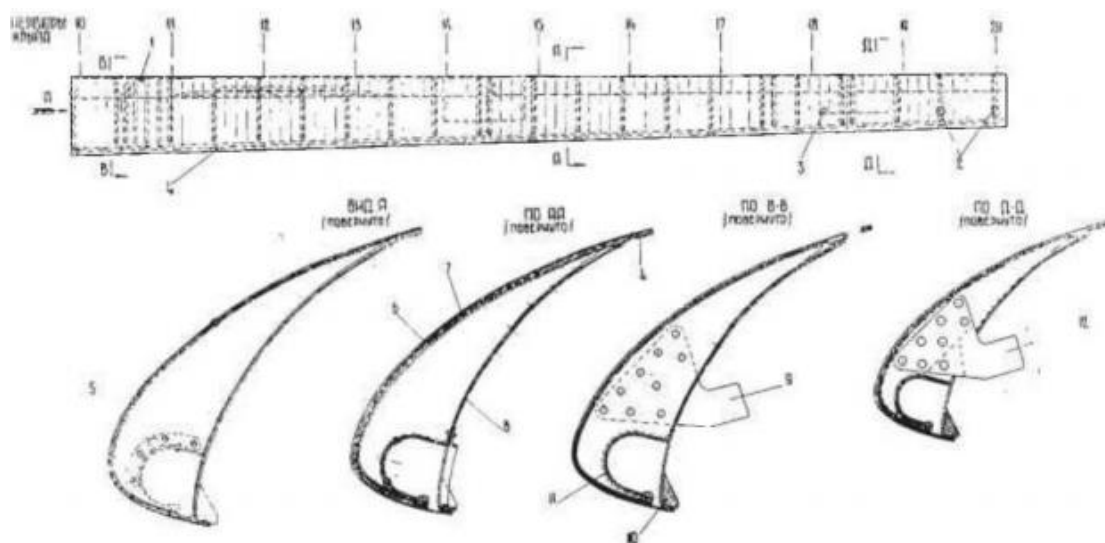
Предкрилок консольної частини крила (1 секція): 1-гофр; 2-нервюри; 3- дуралюмінієві прокладки; 4-прокладки з полімідної смоли; 5- окантовка; 6-верхня обшивка; 7-гофр; 8 нижня обшивка; 9-кронштейн на нервюрі 11; 10- прокладка з пінопласту ЛХВ-1, обклеєна капроною тканиною; 11-облицьовка з стеклотканини; кронштейн на нервюрі 19.
